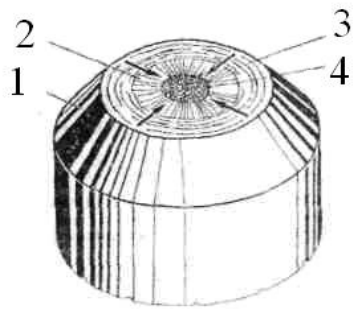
Схема будови поверхні злому при розтягуванні циліндричного зразка з надрізом:
